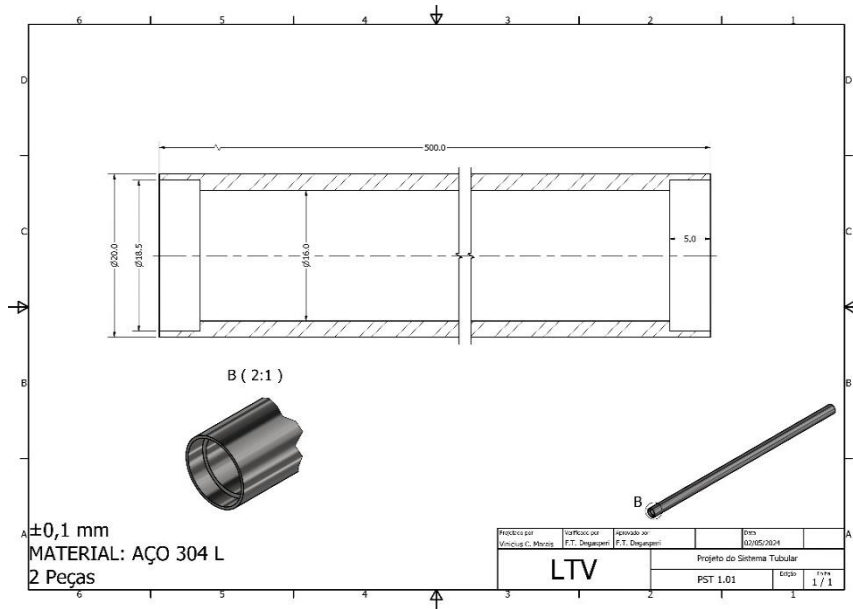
Inserção das cotas e textos no desenho técnico do objeto selecionado.
